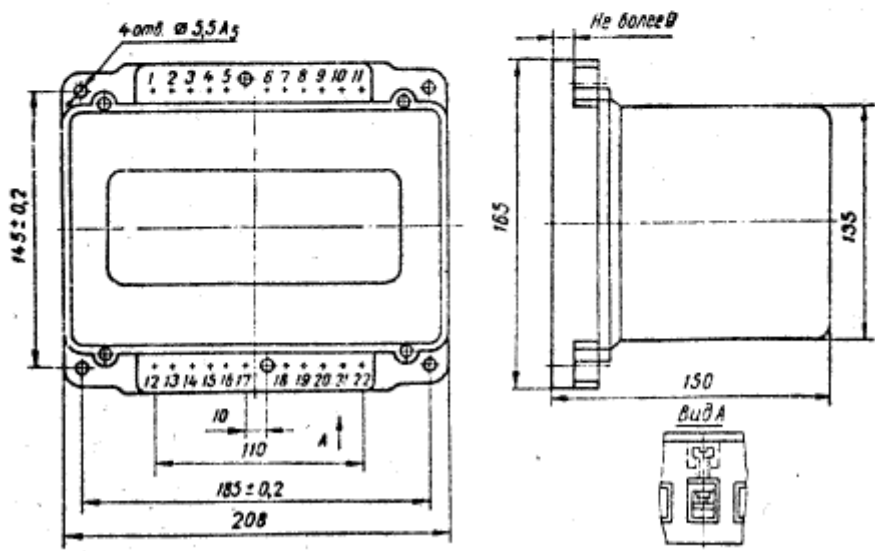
Габаритные и установочные размеры реле BC-10-62+68
